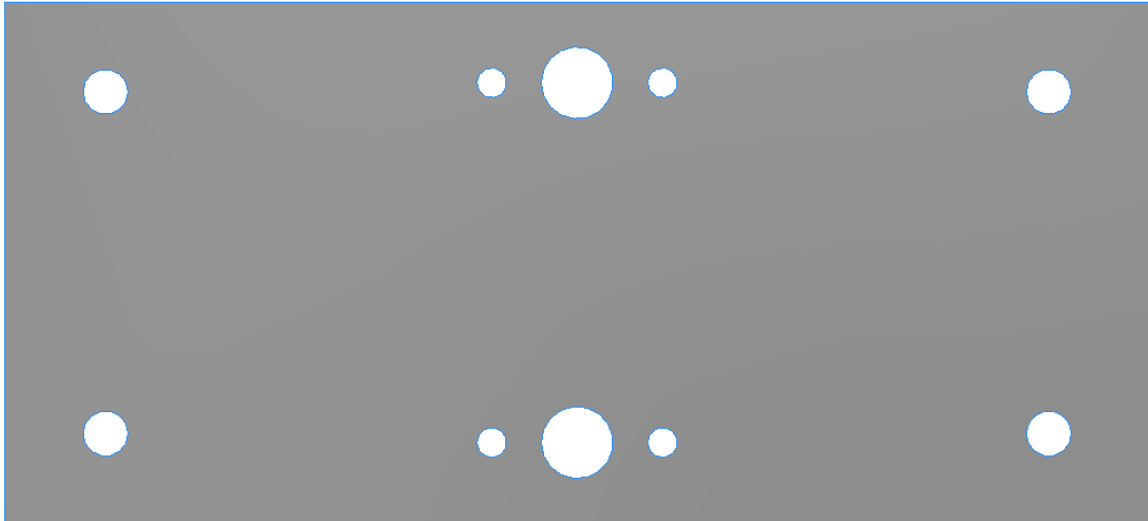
Podložka pro šroub na upevnění hřídele [autor]
